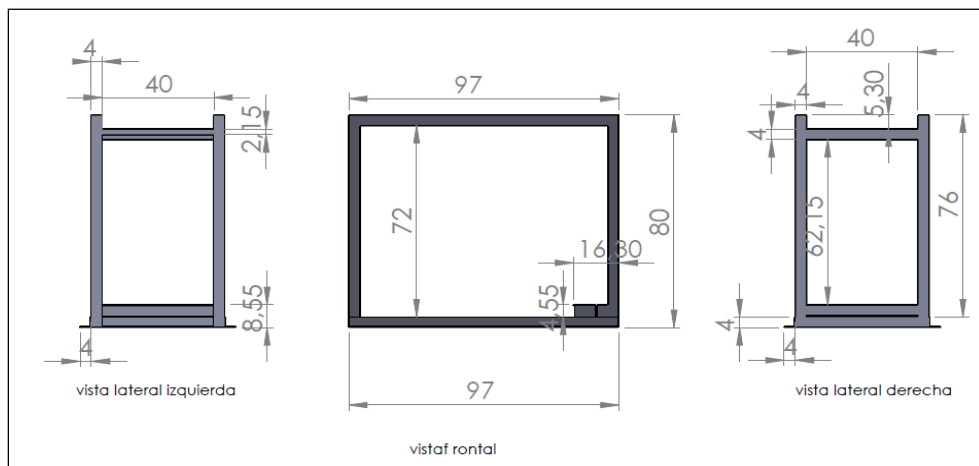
Diseño de la base de la máquina y del motor, con sus medidas en cm.
